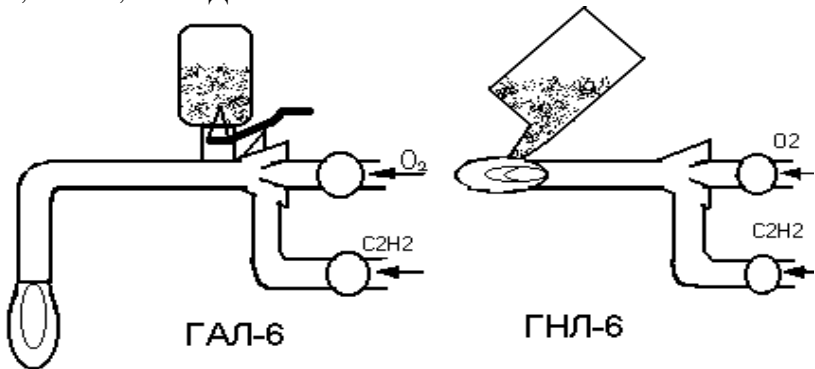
Схеми пальників для газопорошкового наплавлення
